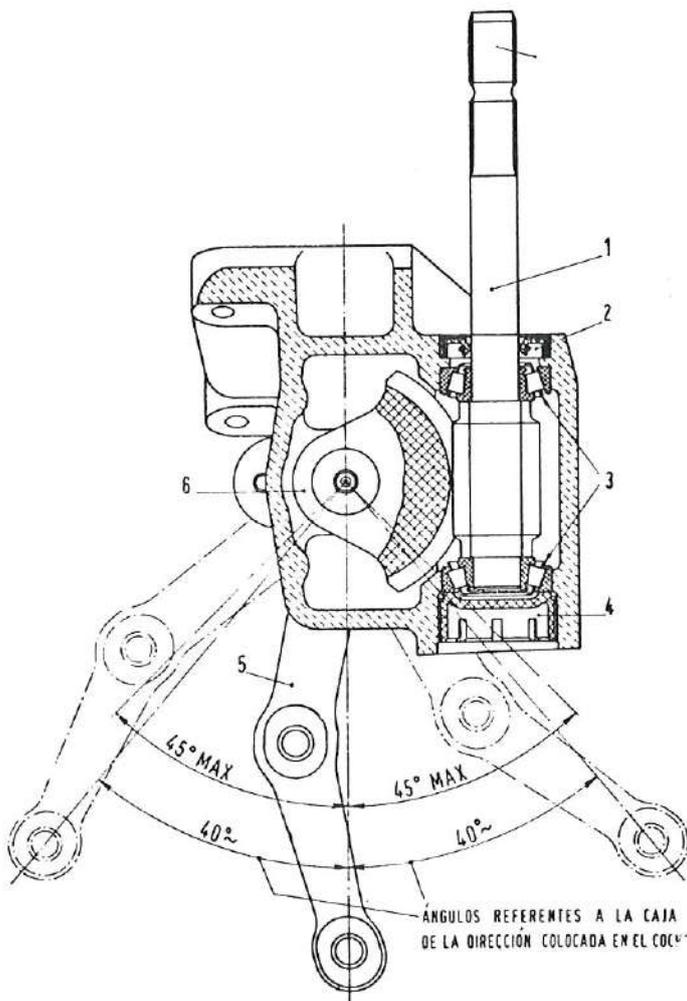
Sección de la caja de dirección sobre el tornillo sin fin.
